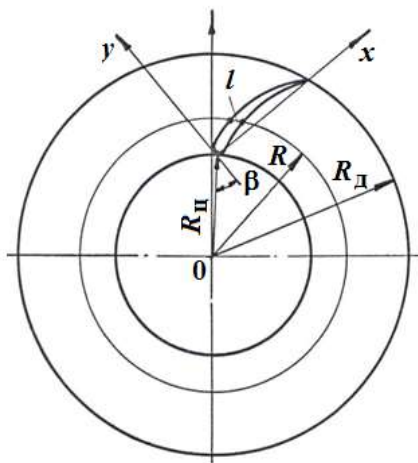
Расположение и установка лопатки на диске рабочего колеса вентилятора
